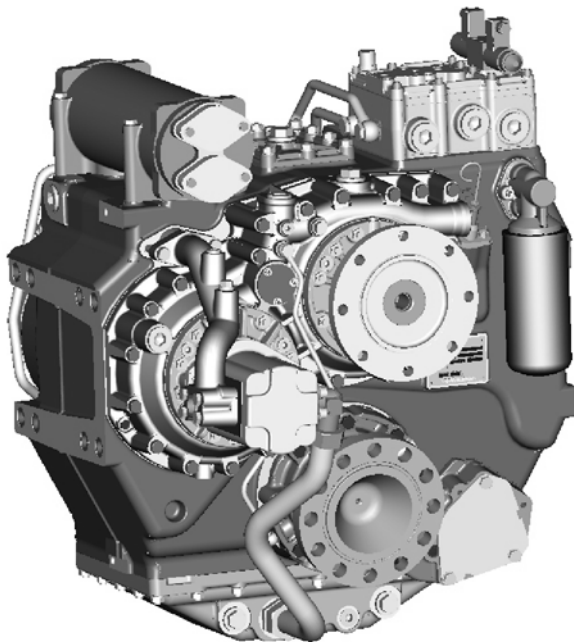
Getriebe ZF 3000 V (Beispiel)
